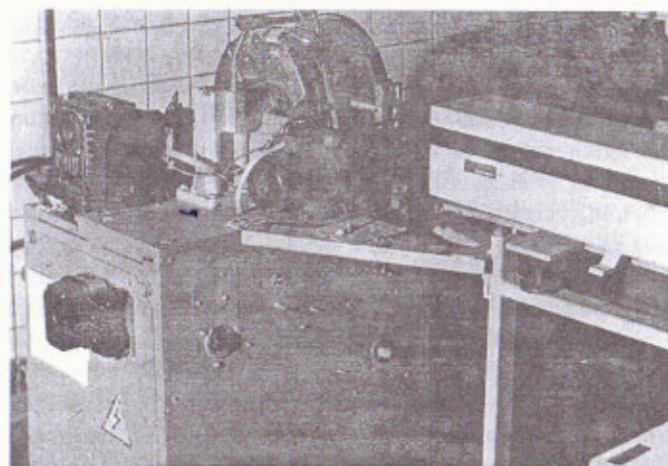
Общий вид установки резки колец для плоской ножки ЭОС В2.М3.104.012
